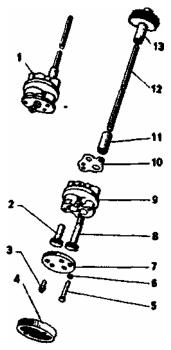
Детали масляного насоса: 1 - масляный насос; 2 - шестерня масляного насоса; 3 - болт крепления крышки корпуса (2 шт ); 4 - фильтр масляного насоса; 5 - болт М6х50 крепления масляного насоса (2 шт.); 6 - шайба 6Л (2 шт.); 7 - крышка насоса; 8 - шестерня масляного насоса ведущая; 9 - корпус масляного насоса; 10 - прокладка; II - муфта соединительная шестерни ведущей; 12 - штанга соединительная шестерни ведущей; 13 - шестерня ведущая масляного насоса
